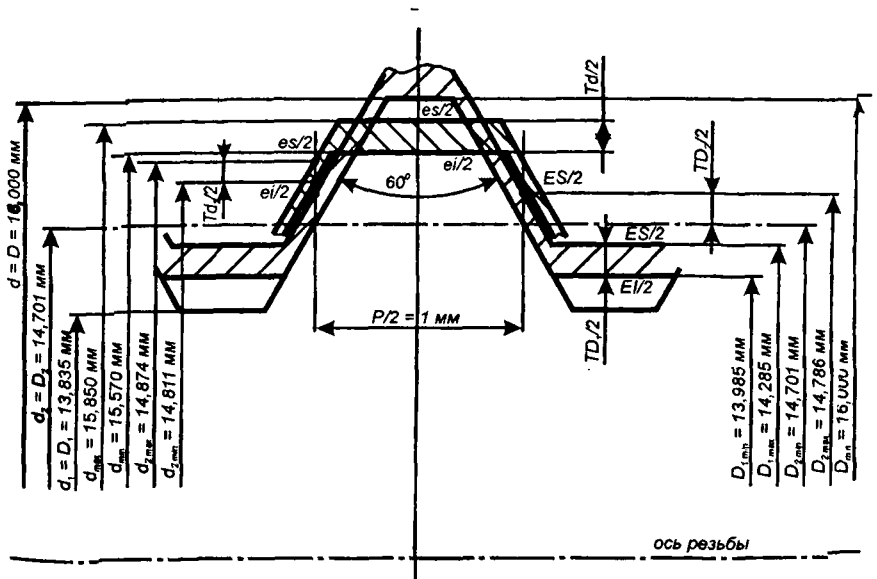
Схема расположения полей допусков резьбового соединения  $M16 - 2H5C/2r$
